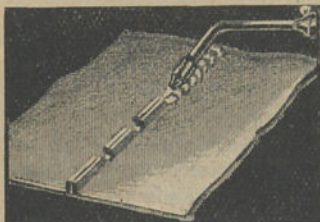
Soldadura de chapas finas com os bordos curvados.
